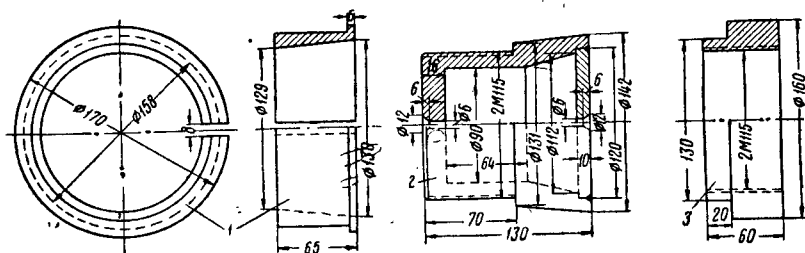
Детали приспособления для самоцентрировки подшипникового щита:
